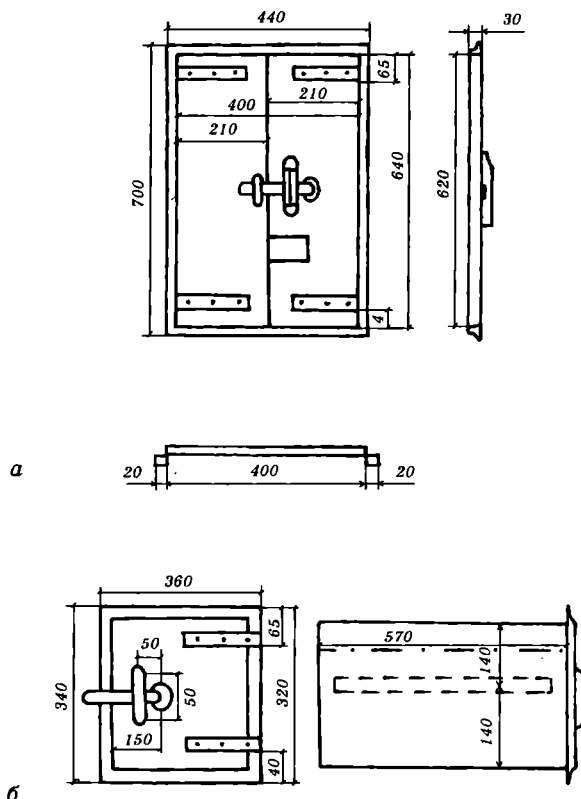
Изготовление дверок, решеток, водогрейной коробки для отопительно-варочной печи:
